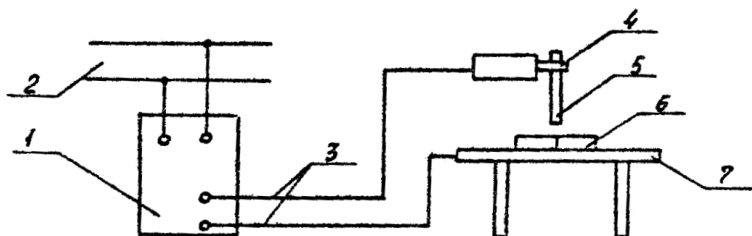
Схема сварочного поста для РДС:
